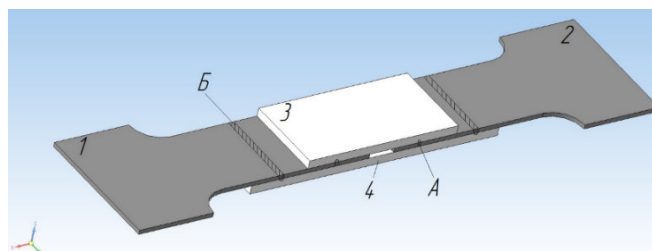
Контрольный образец: 1 и 2 – листы стали 20, 3 и 4 – листы из алюминиевого сплава АМг2М, А и Б – места соединений
